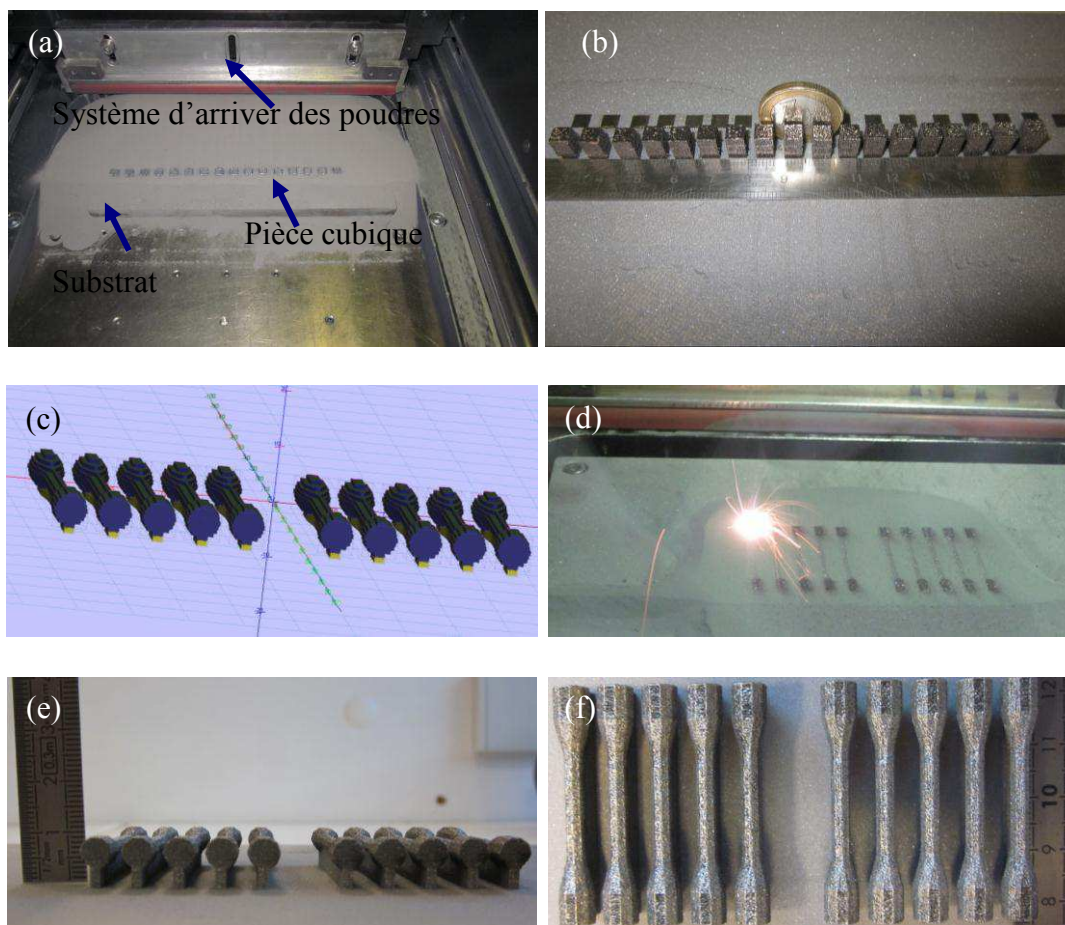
Photos de (a) chambre de fabrication et (b) éprouvettes cubiques; (c) modèle CAO d'éprouvettes de traction, (d) photo montrant le processus en cours de fabrication d'éprouvettes de traction (e) vue de profil (f) vue de dessus des éprouvettes de traction sur la plate-forme de fabrication.
